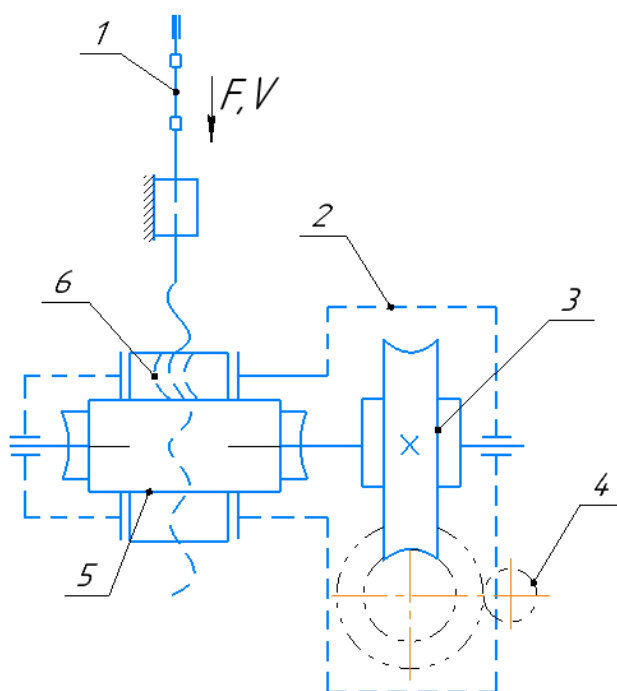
Кінематична схема приводу: 1 – зразок; 2 – корпус; 3 – черв'ячна передача; 4 – циліндрична передача; 5 – черв'ячна передача; 6 – передача гвинт-гайка.
